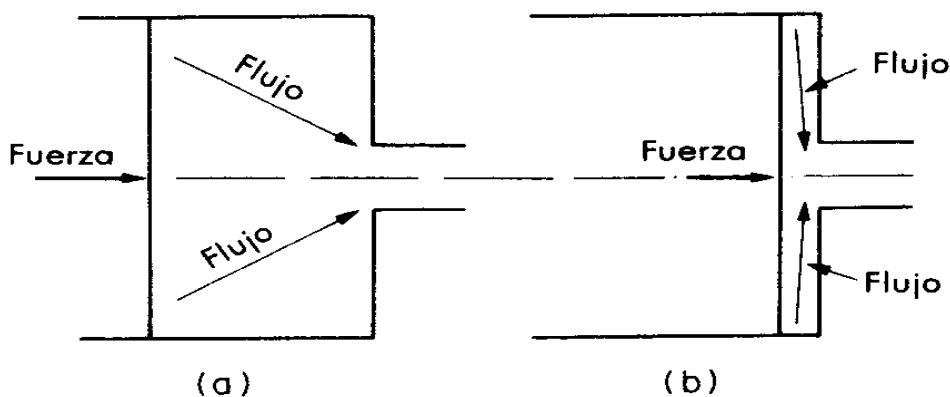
Esquema del flujo y la fuerza en un proceso de extrusión.
